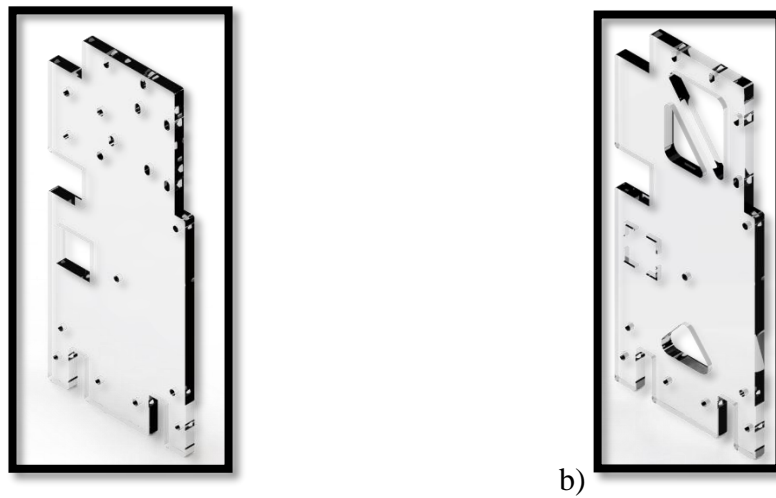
Placas de PMMA para una columna de la estructura Gantry, a) Columna lateral, b) Columna lateral posterior.
